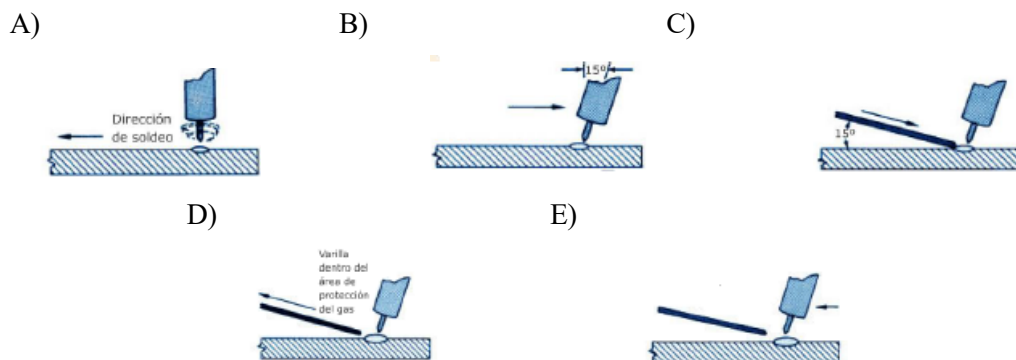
Técnica para realizar el soldeo TIG manual [7]
